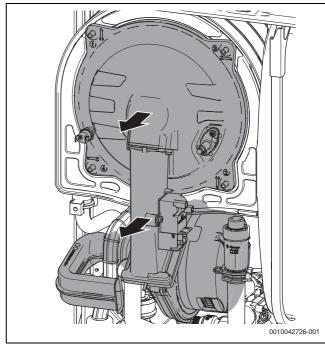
Smontaggio del gruppo sportello della camera di combustione
